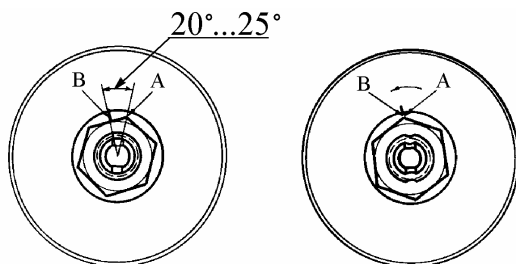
Затягивание и регулировка подшипников ступицы переднего колеса:
